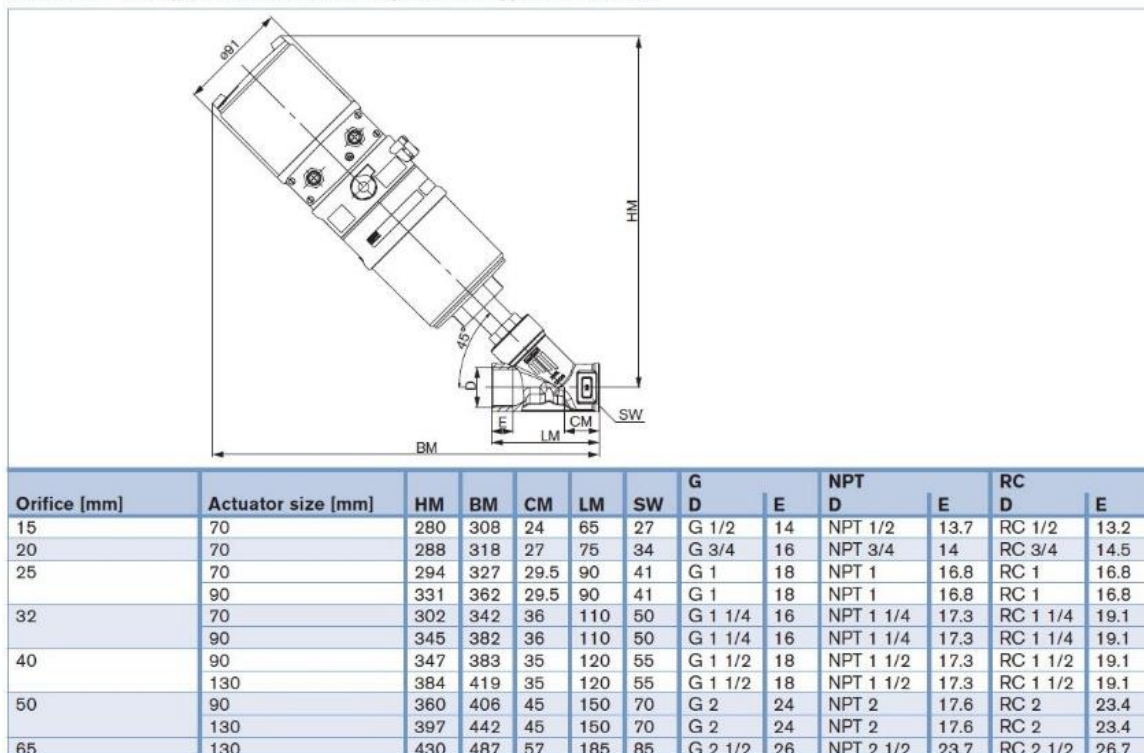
dimensioni della valvola ELEMENT 8802-YG
